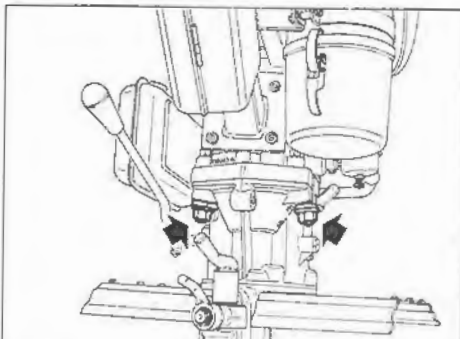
Viti scomposizione macchina in due parti - Schrauben für Zerlegen der Maschine in zwei Teile - Tornillos para desmontar la máquina en dos partes
